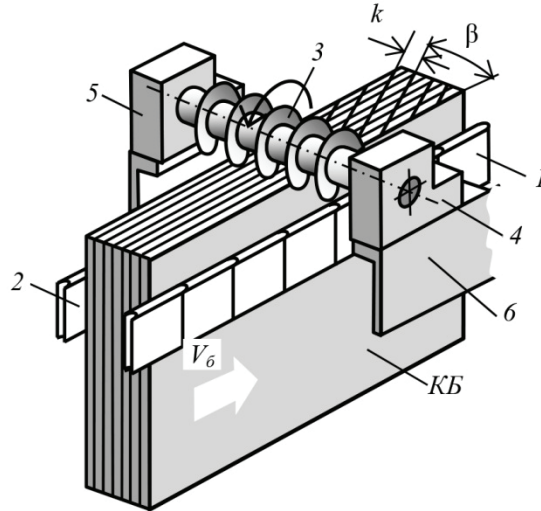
Принципова схема пристрою для підготовки корінця книжкового блока до нанесення клею для незшивного скріплення
